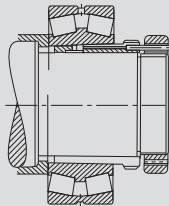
Desmontagem da Luva de Remoção com o uso de Pressão Hidráulica
